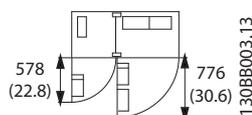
Пространство перед корпусом IP21/IP54, типоразмер F9
